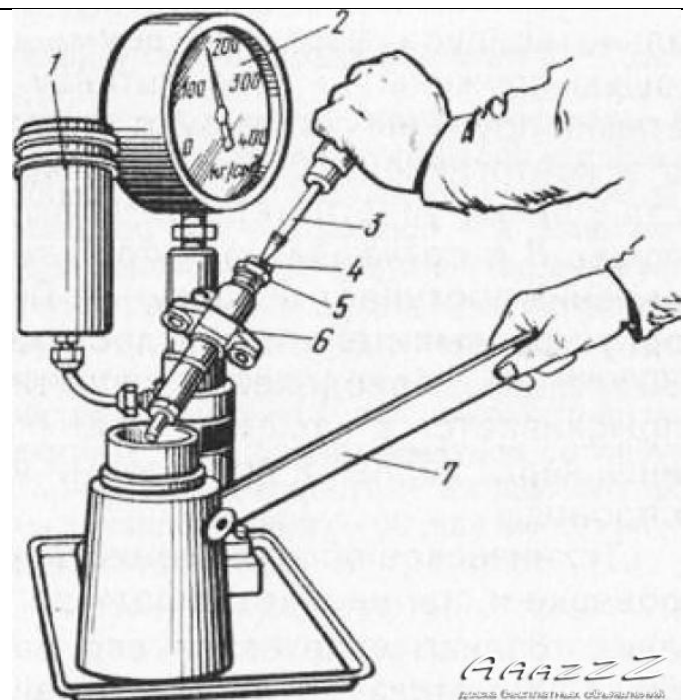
Стенд для регулировки форсунок дизельного двигателя.
